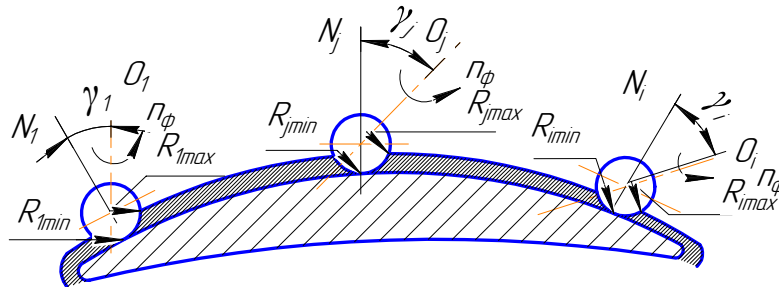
Схема положений инструмента со сферической режущей поверхностью на поверхности заготовки
